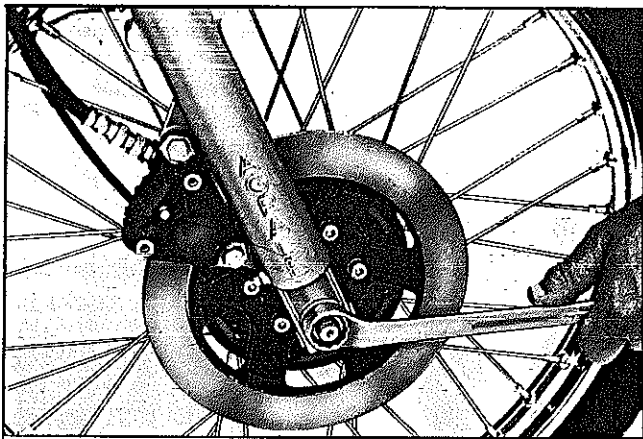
DESMONTAGEM DA RODA DIANTEIRA
